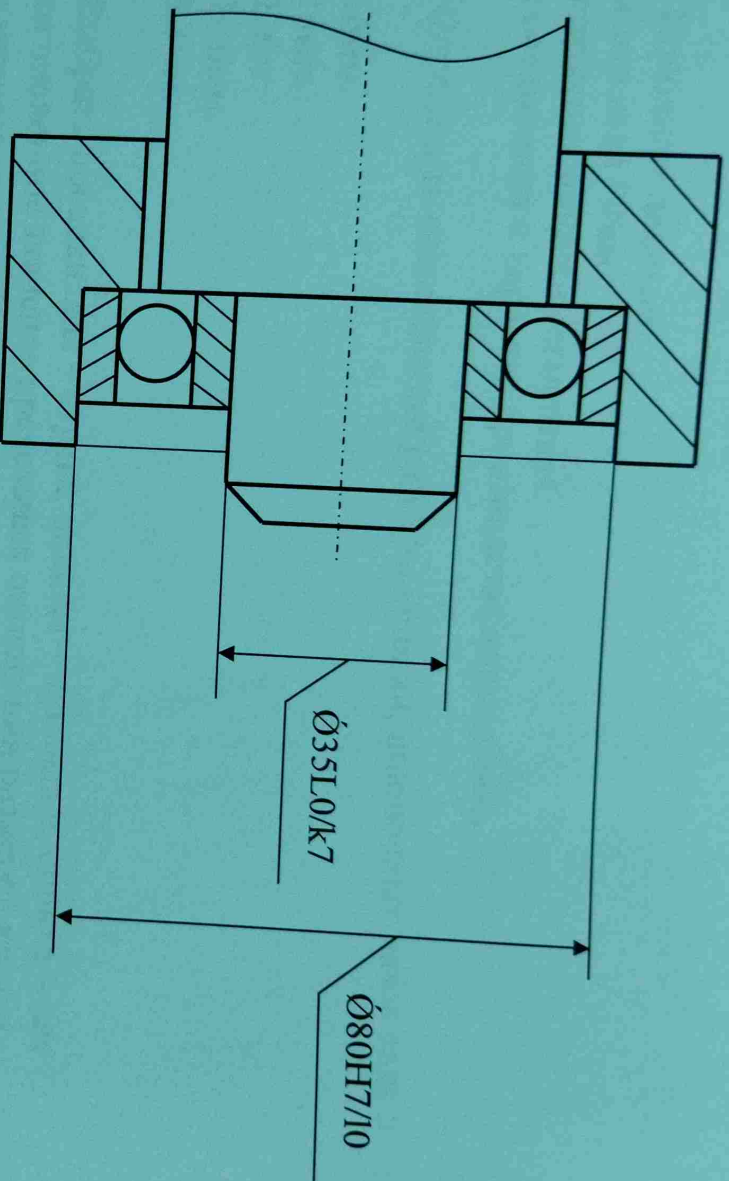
в - Эскиз соединения в сборе для подшипникового узла.
